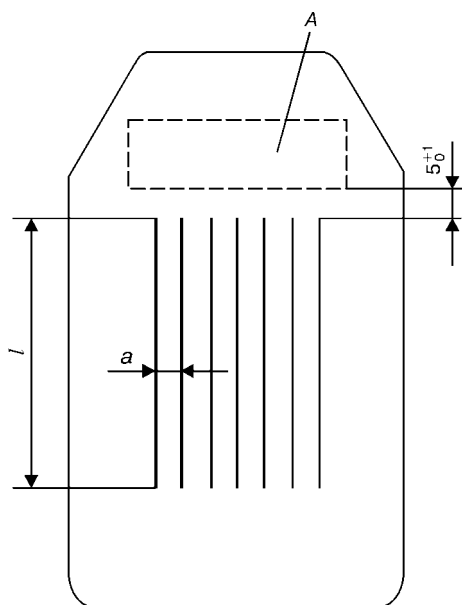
Индикатор качества изображения проволоочного типа по стандарту ДСТУ EN 462-1: А — поле для маркировки
